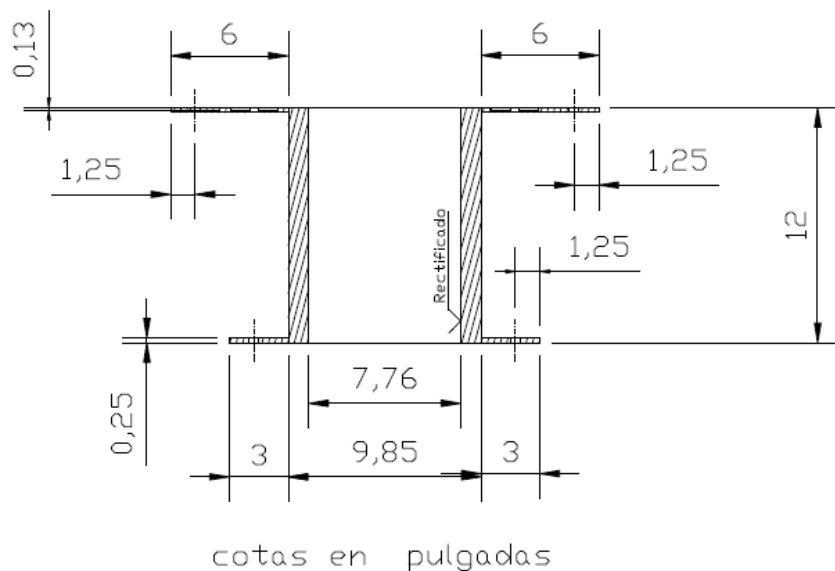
, se muestran las dimensiones finales que deberá tener el bushing.
